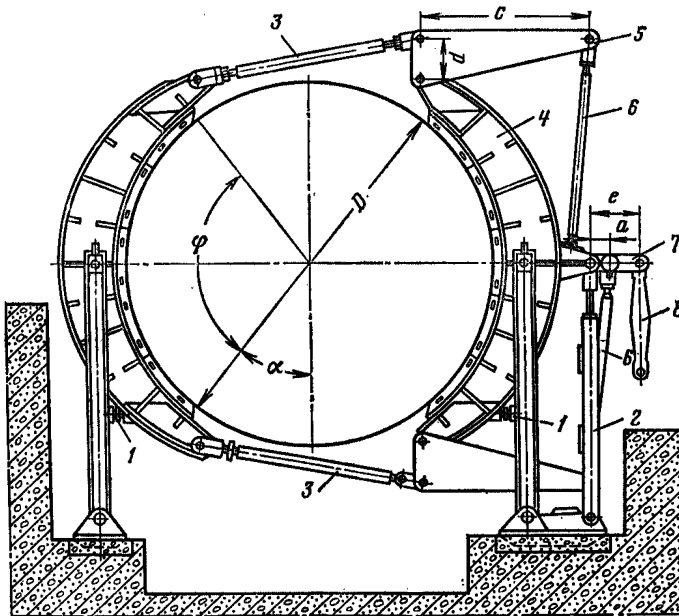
Схема исполнительного органа тормоза подъемных машин НКМЗ (II типа): 1 — упорные болты; 2 — винтовая стойка; 3, 6, 8 — тяги; 4 — тормозные балки; 5 и 7 — рычаги
